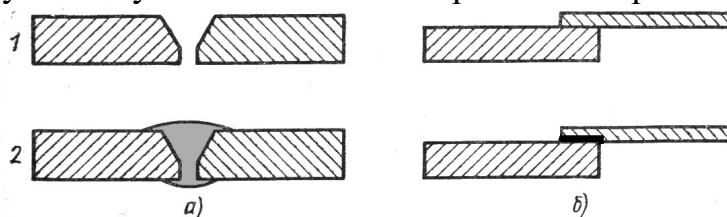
Схема пайки-сварки (а) и сварки-пайки (б)
